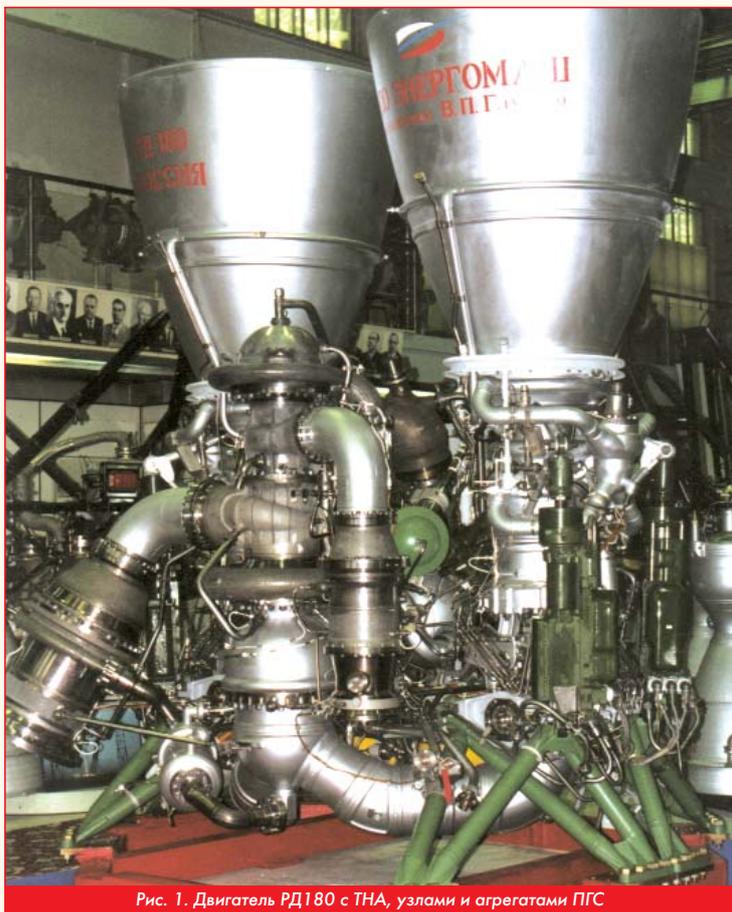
Двигатель РД180 с ТНА, узлами и агрегатами ПГС
